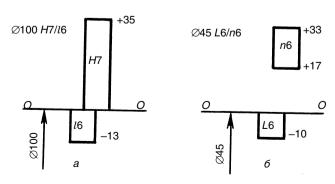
Схемы расположения полей допусков посадок подшипника качения:
